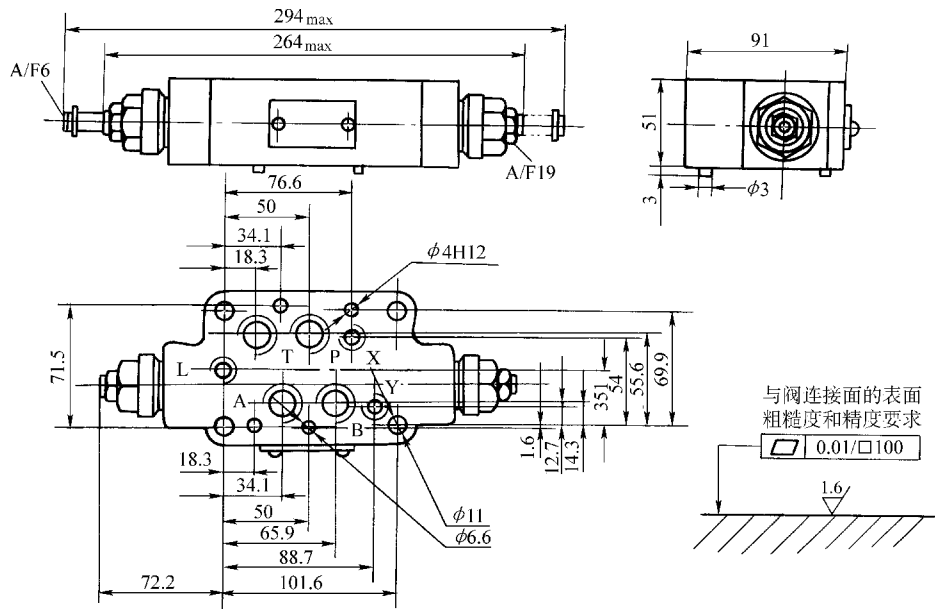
Z2FS16 型叠加式节流阀的外形尺寸
